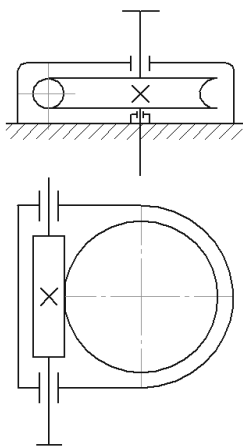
Одноступенчатый червячный редуктор с вертикальным расположением вала червяка
